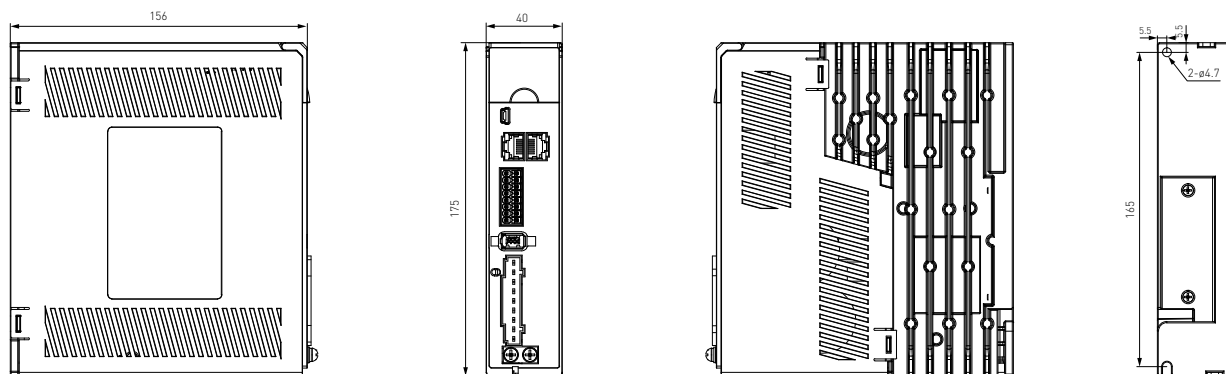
Габаритные размеры драйвера EL7-EC400F (размер A).
